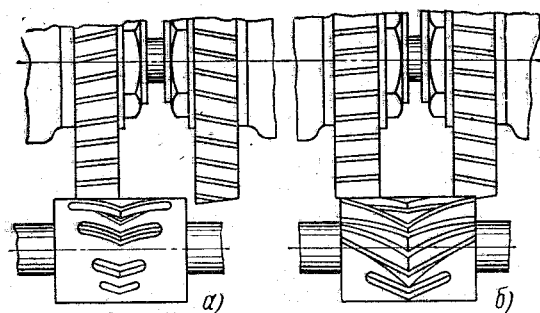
Схема нарезания шевронных колес двумя долбяками:
